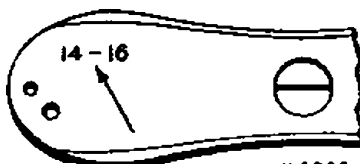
Размеры игл, обозначенные на игольной пластинке.
